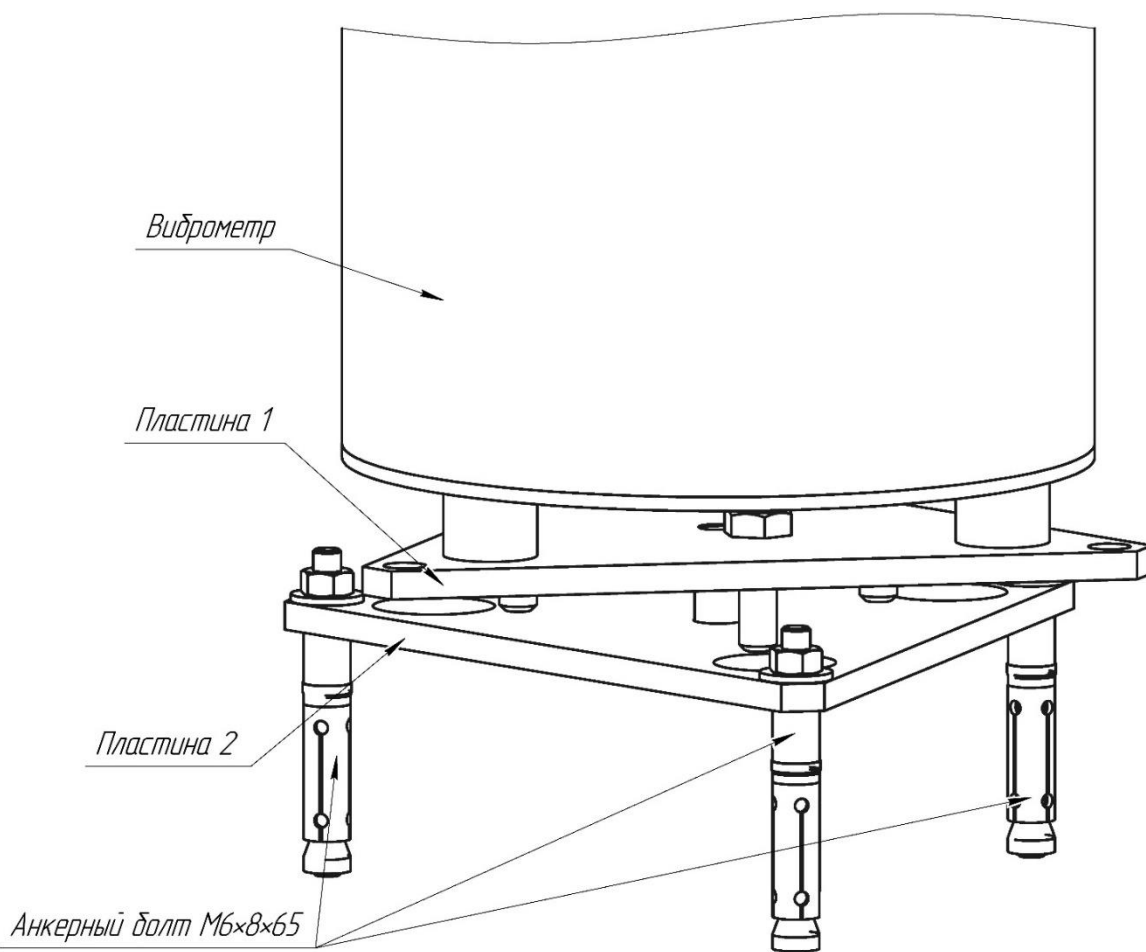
Крепление виброметра с регулировкой – Шаг 3
